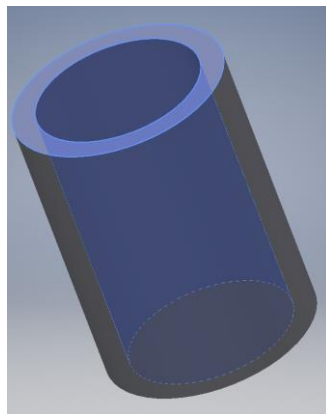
Piesă presare matriță multicavă (desen execuție planșa 9/16)
